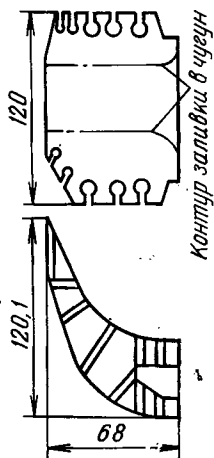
Лопатка литой диафрагмы, изготовляемая фрезерованием
